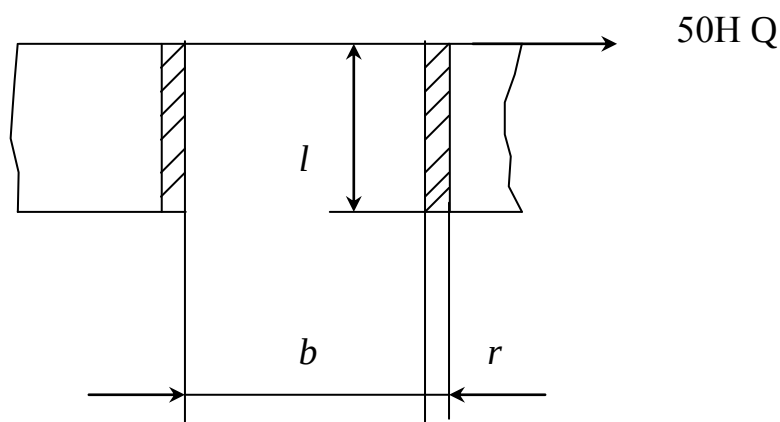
Схема для расчета сварочного соединения
